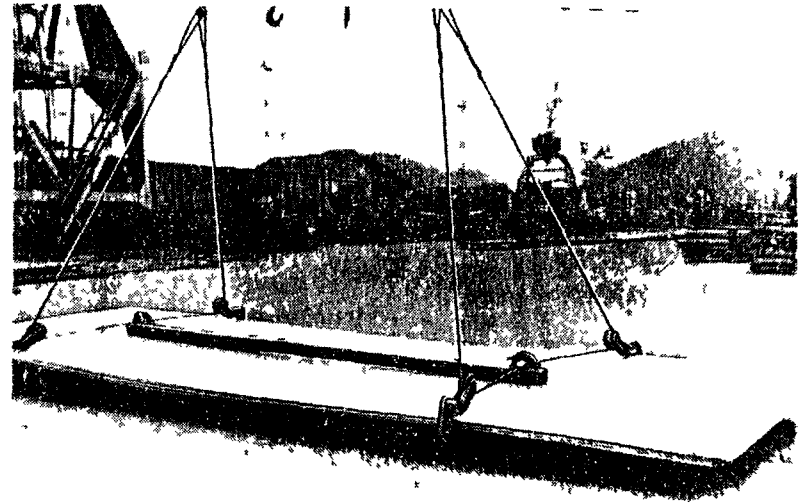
М 1 Строповка «подъема» крановыми захватами с прижимной балкой для перегрузки стали толстолистовой без упаковки
